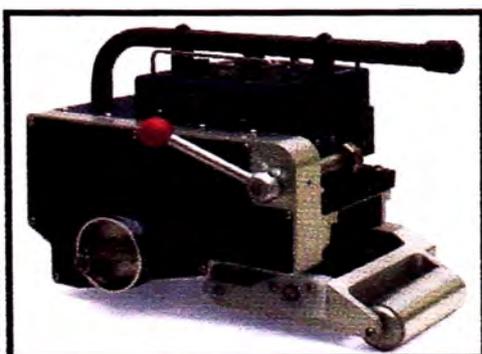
Esquema de Soldadura por Extrusión
